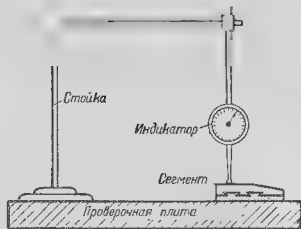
Проверка индикатором толщины сегментов упорного подшипника
